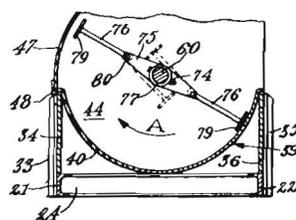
Ein Schnitt entsprechend Bild 6 oder 7. Streuwerkzeuge aus gelenkig miteinander verbundenen Armstücken
